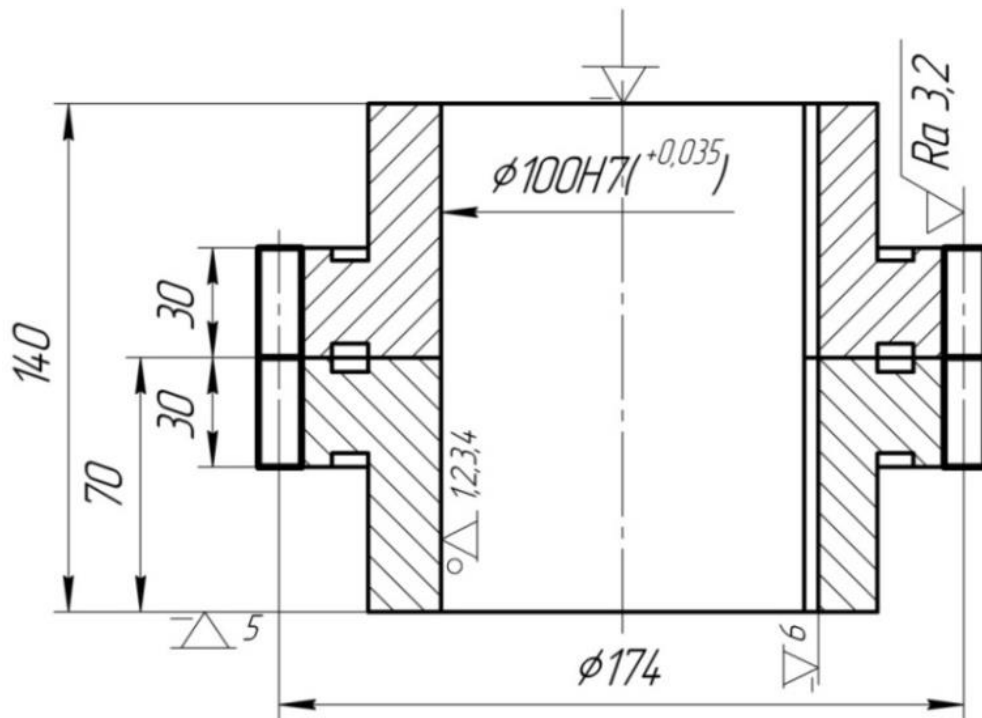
Ескіз заготовки на операції 025. Зубофрезерна
